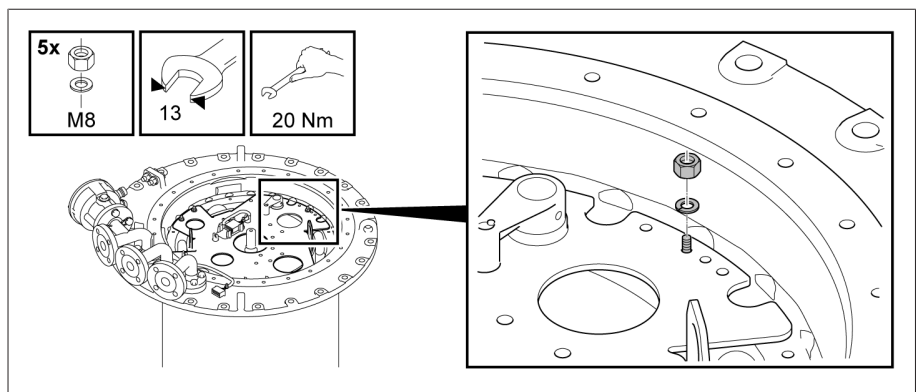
Placa de soporte del cuerpo insertable del ruptor
